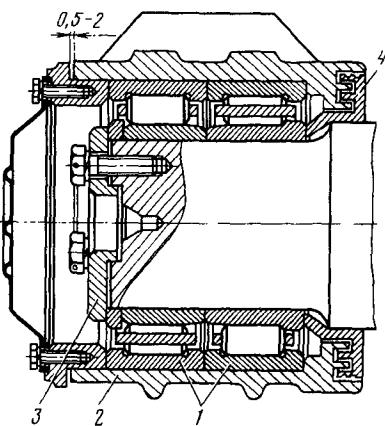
Букса с двумя цилиндрическими подшипниками на горячей посадке с торцовым креплением шайбой:
